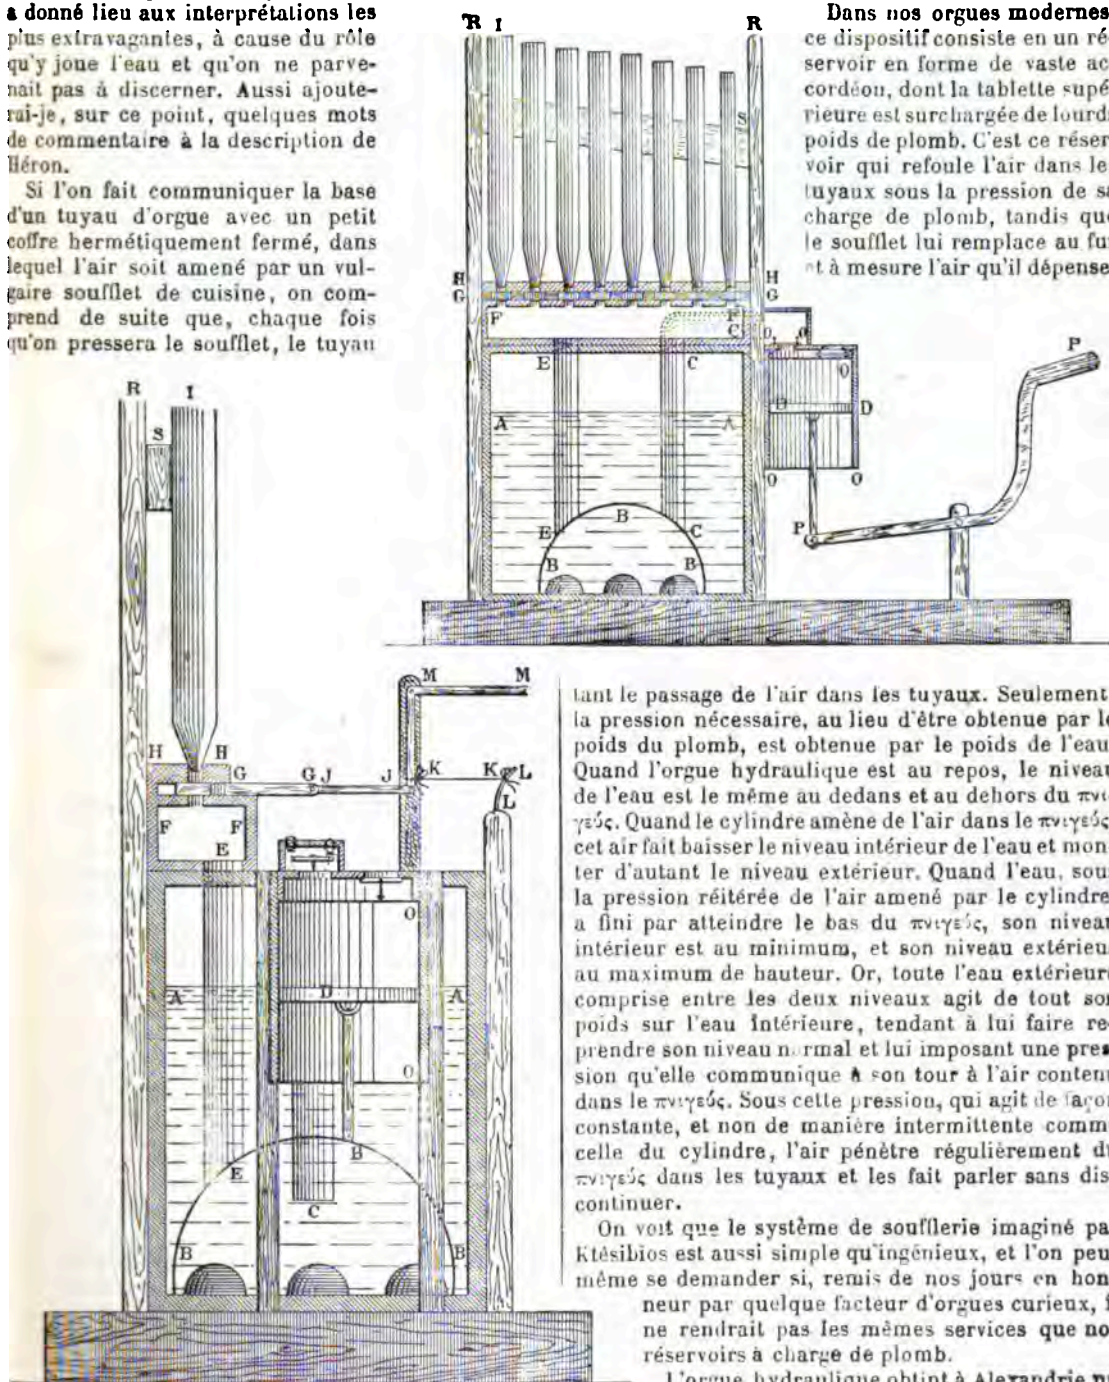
L'orgue hydraulique vu de face et de profil.
